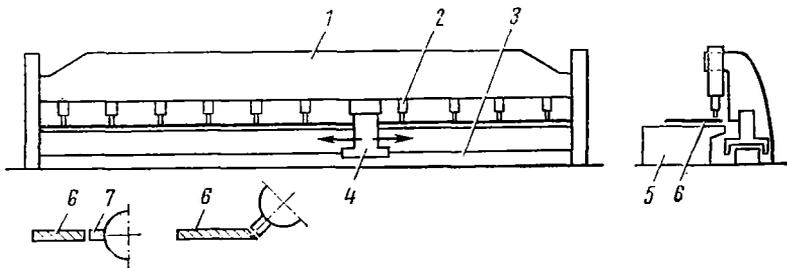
Кромкострогальный станок и детали положения реза при прямой строжке и с образованием разделки под сварку.
